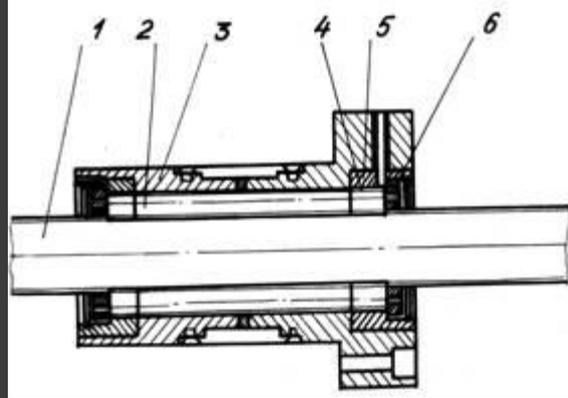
Передача винт – гайка с короткими резьбовыми роликами и двумя полугайками с выборкой зазора:
